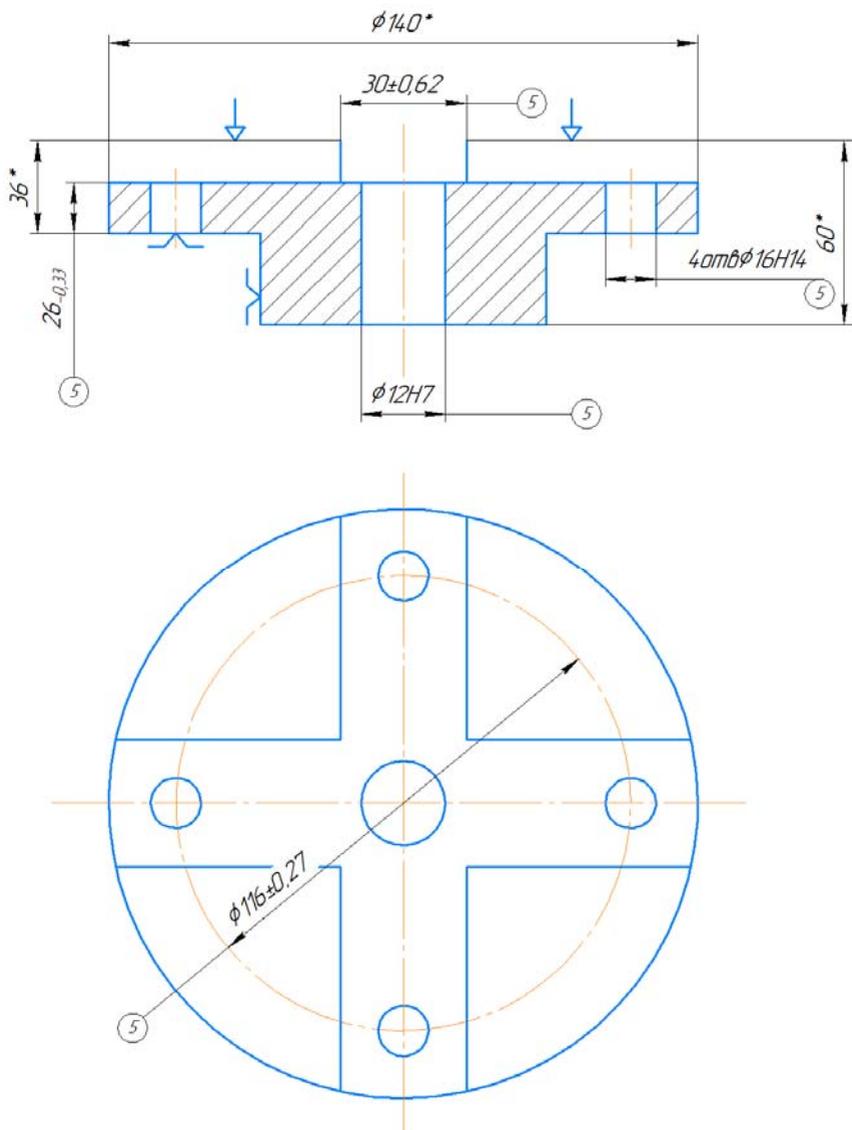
Эскизы заготовки из латуни ЛС59-1 и комплексной операции обработки детали «Втулка» на станке модели 2254ВМФ4
